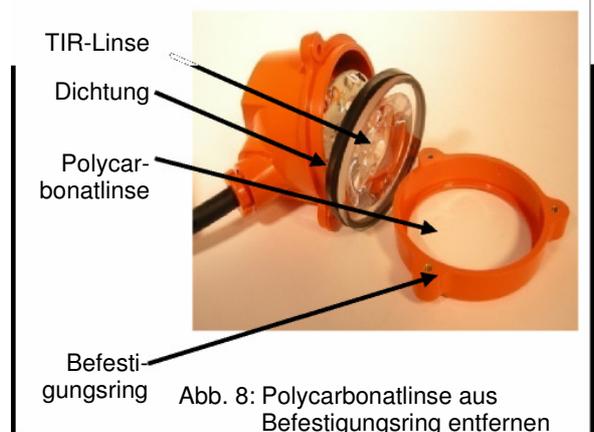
Polycarbonatlinse aus Befestigungsring entfernen
